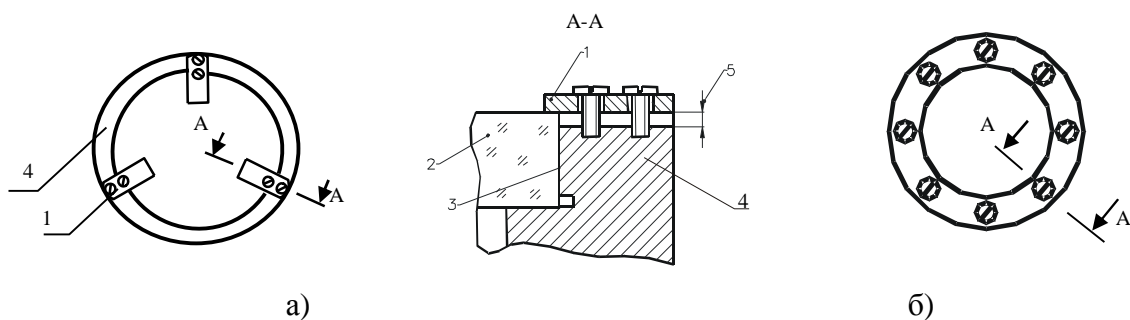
Кріплення пружинними планками і мембранами: а – пружинна планка; б – мембрана; 1 – пружинна планка; 2 – скло; 3 – зовнішня точна посадка; 4 – оправа; 5 – гарантований зазор
